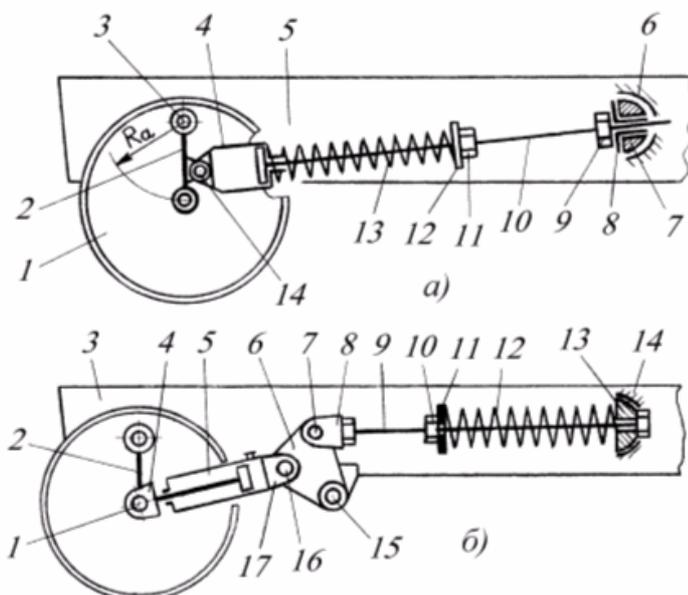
Принципиальные схемы конструкций натяжного и амортизирующего устройств, устанавливаемых на раме трактора
